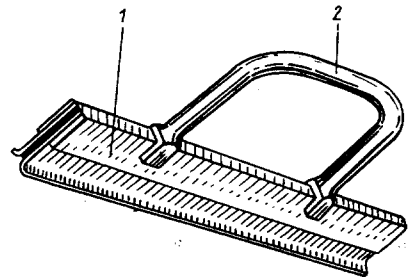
Обойма для отгиба триммеров лопастей несущего винта:
